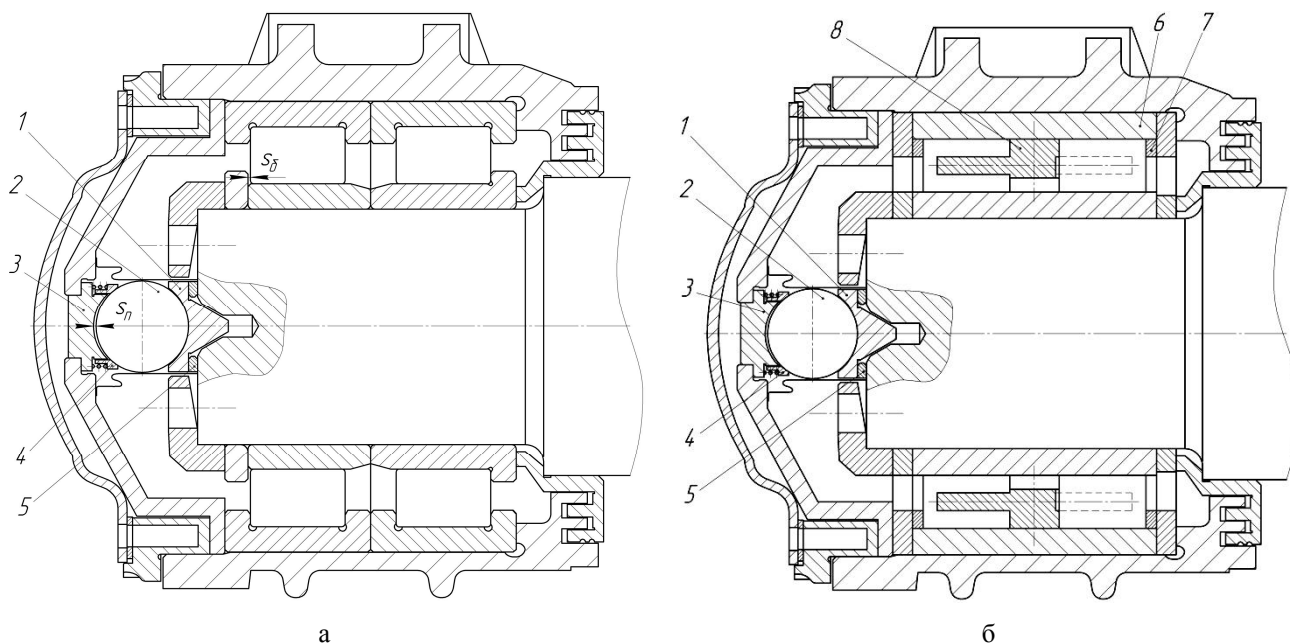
Буксы грузового вагона с торцевым креплением тарельчатой шайбой:
